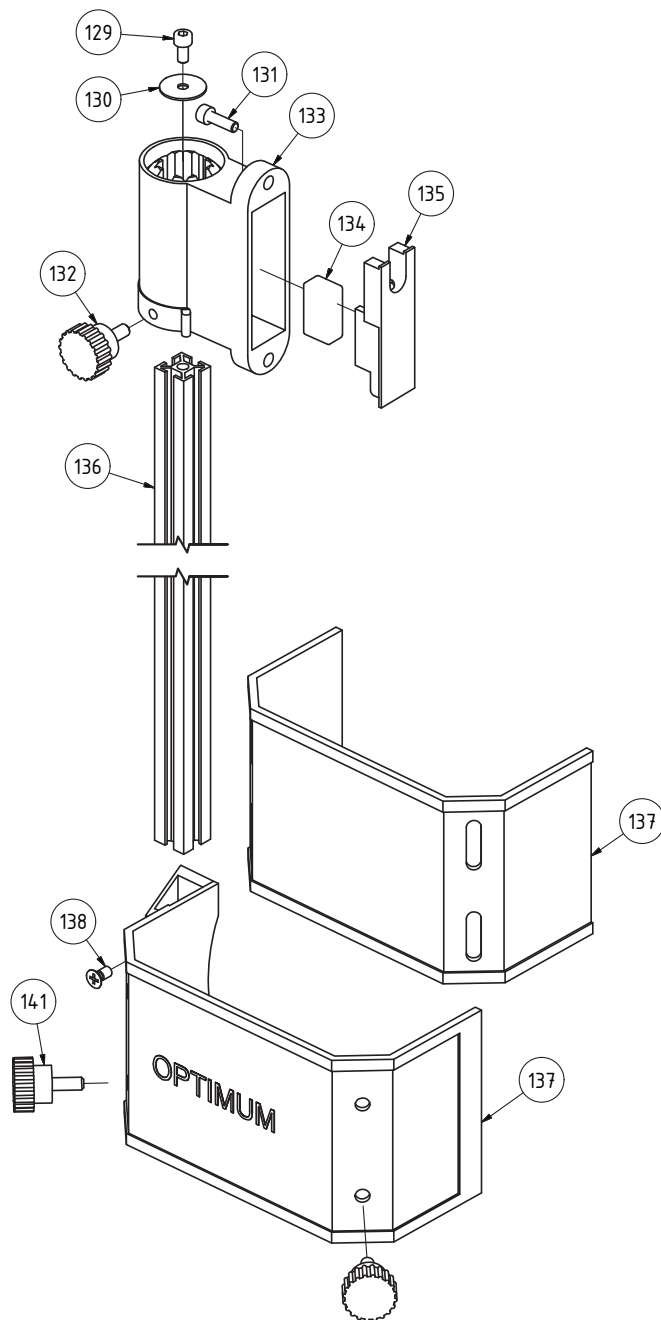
Bohrfutterschutz - Drilling chuck protection
